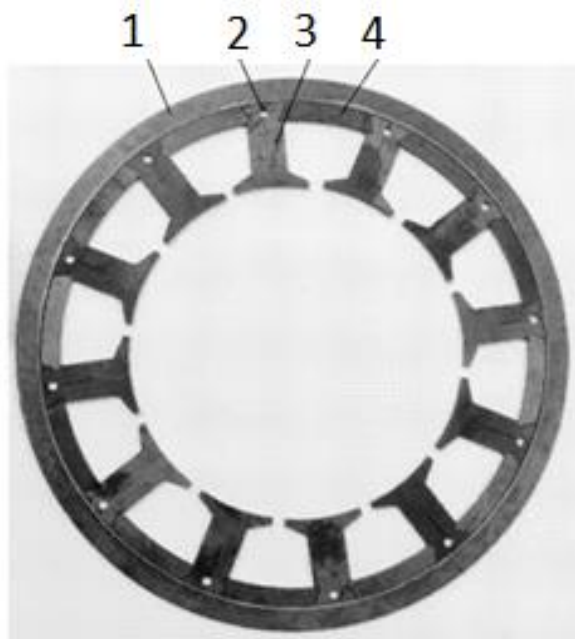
Сборный статор: 1 - корпус; 2 - штифт; 3 - зубец; 4 – спинка статора
